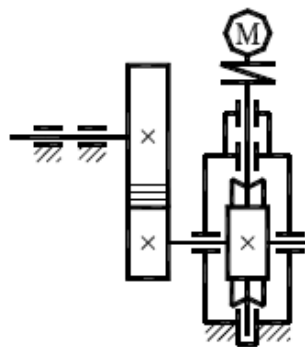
Схема № 1 – Привод, состоящий из червячного редуктора и открытой ременной передачи
